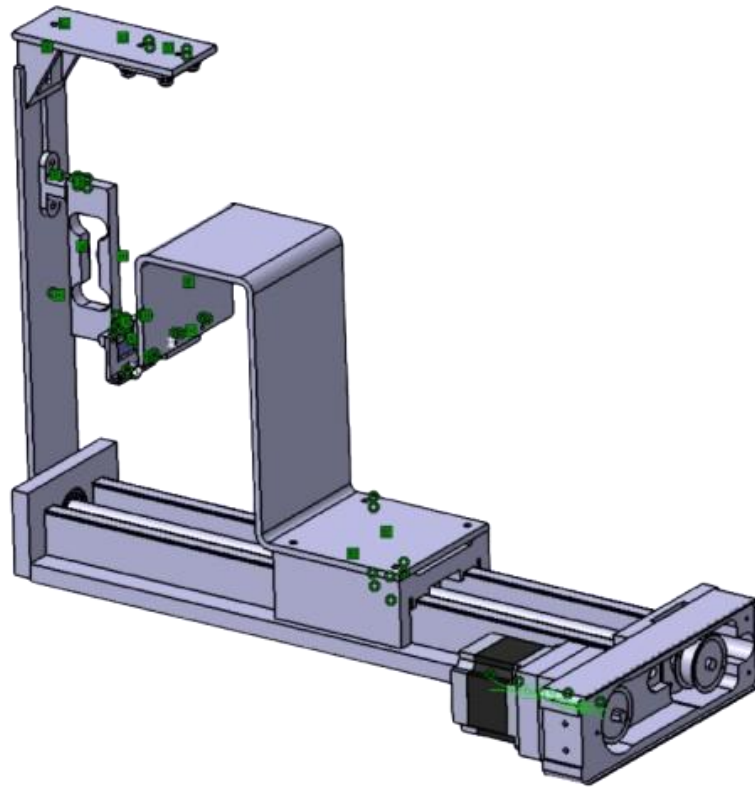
Vue CAO de l'assemblage du banc (CATIA V5).
